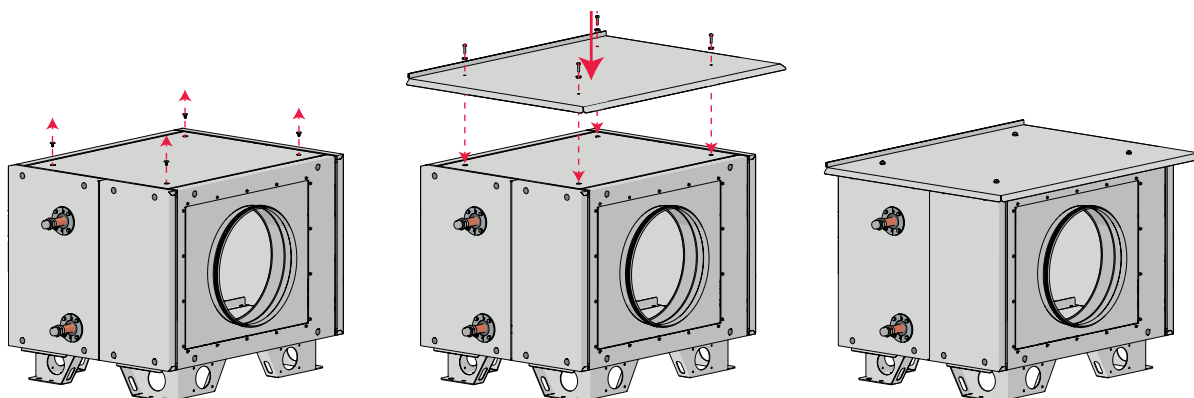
Montage sur le toit d'un dispositif de chauffage/de refroidissement externe
